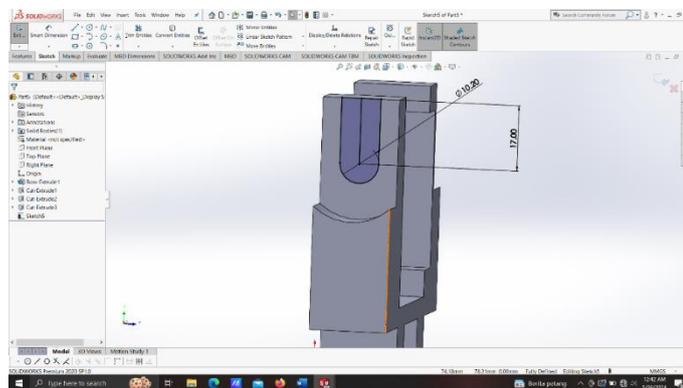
Extruded Cut* Dudukan Motor Servo
